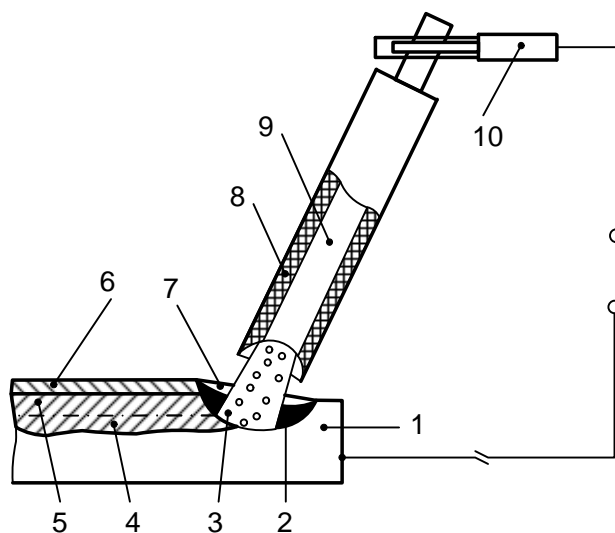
Ручная дуговая сварка штучным электродом: 1 – основной металл; 2 – сварочная ванна; 3 – электрическая дуга; 4 – проплавленный металл; 5 – наплавленный металл; 6 – шлаковая корка; 7 – жидкий шлак; 8 – электродное покрытие; 9 – металлический стержень электрода; 10 – электрододержатель
